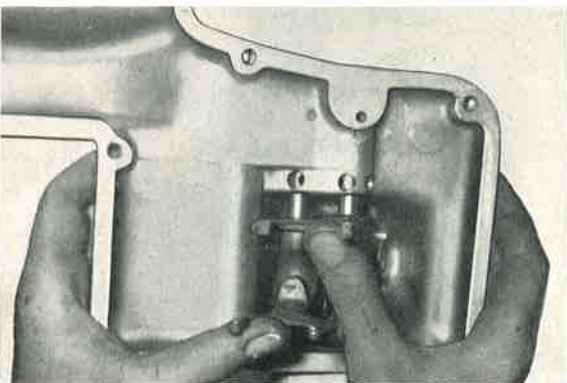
Leerlauf besteht, wenn beide Schaltwellen in ihrer Bohrung die halbmondförmigen Einfräsungen für die Sperrkugeln gegenüberliegend sichtbar werden lassen.
